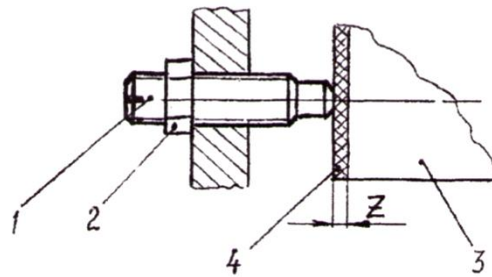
Пример применения регулируемой опоры: 1 – винт установочный; 2 – гайка; 3 – заготовка; 4 – припуск
